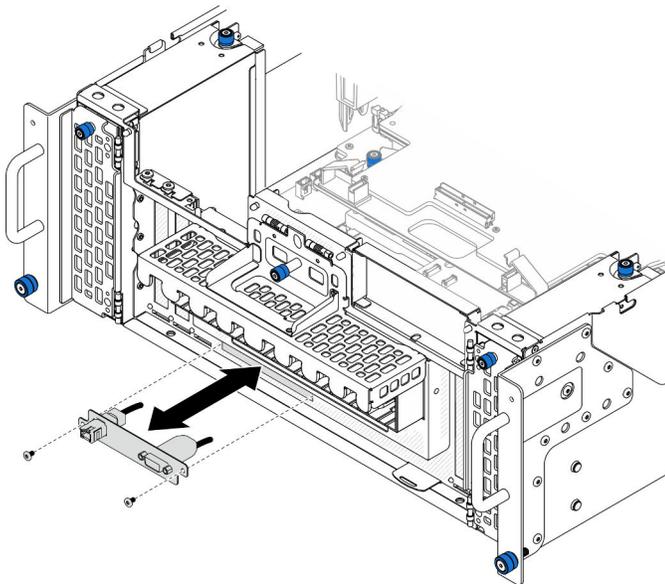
Installieren der seriellen Anschlussbaugruppe
